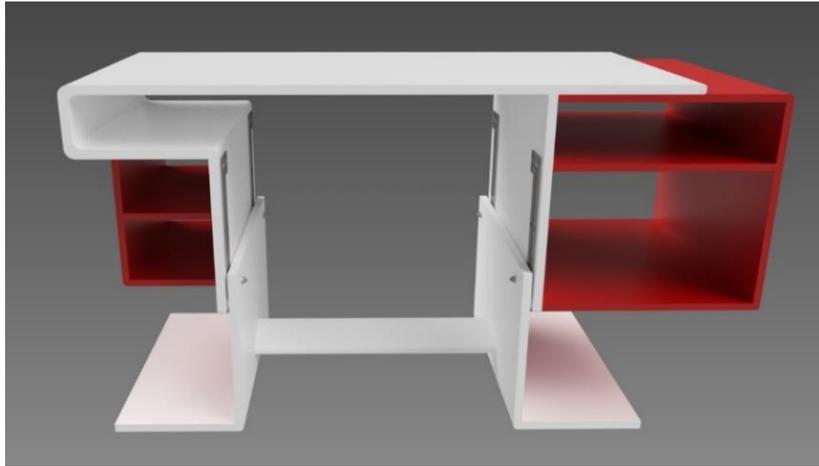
assembly slider pin* pada *sliding sheeter
